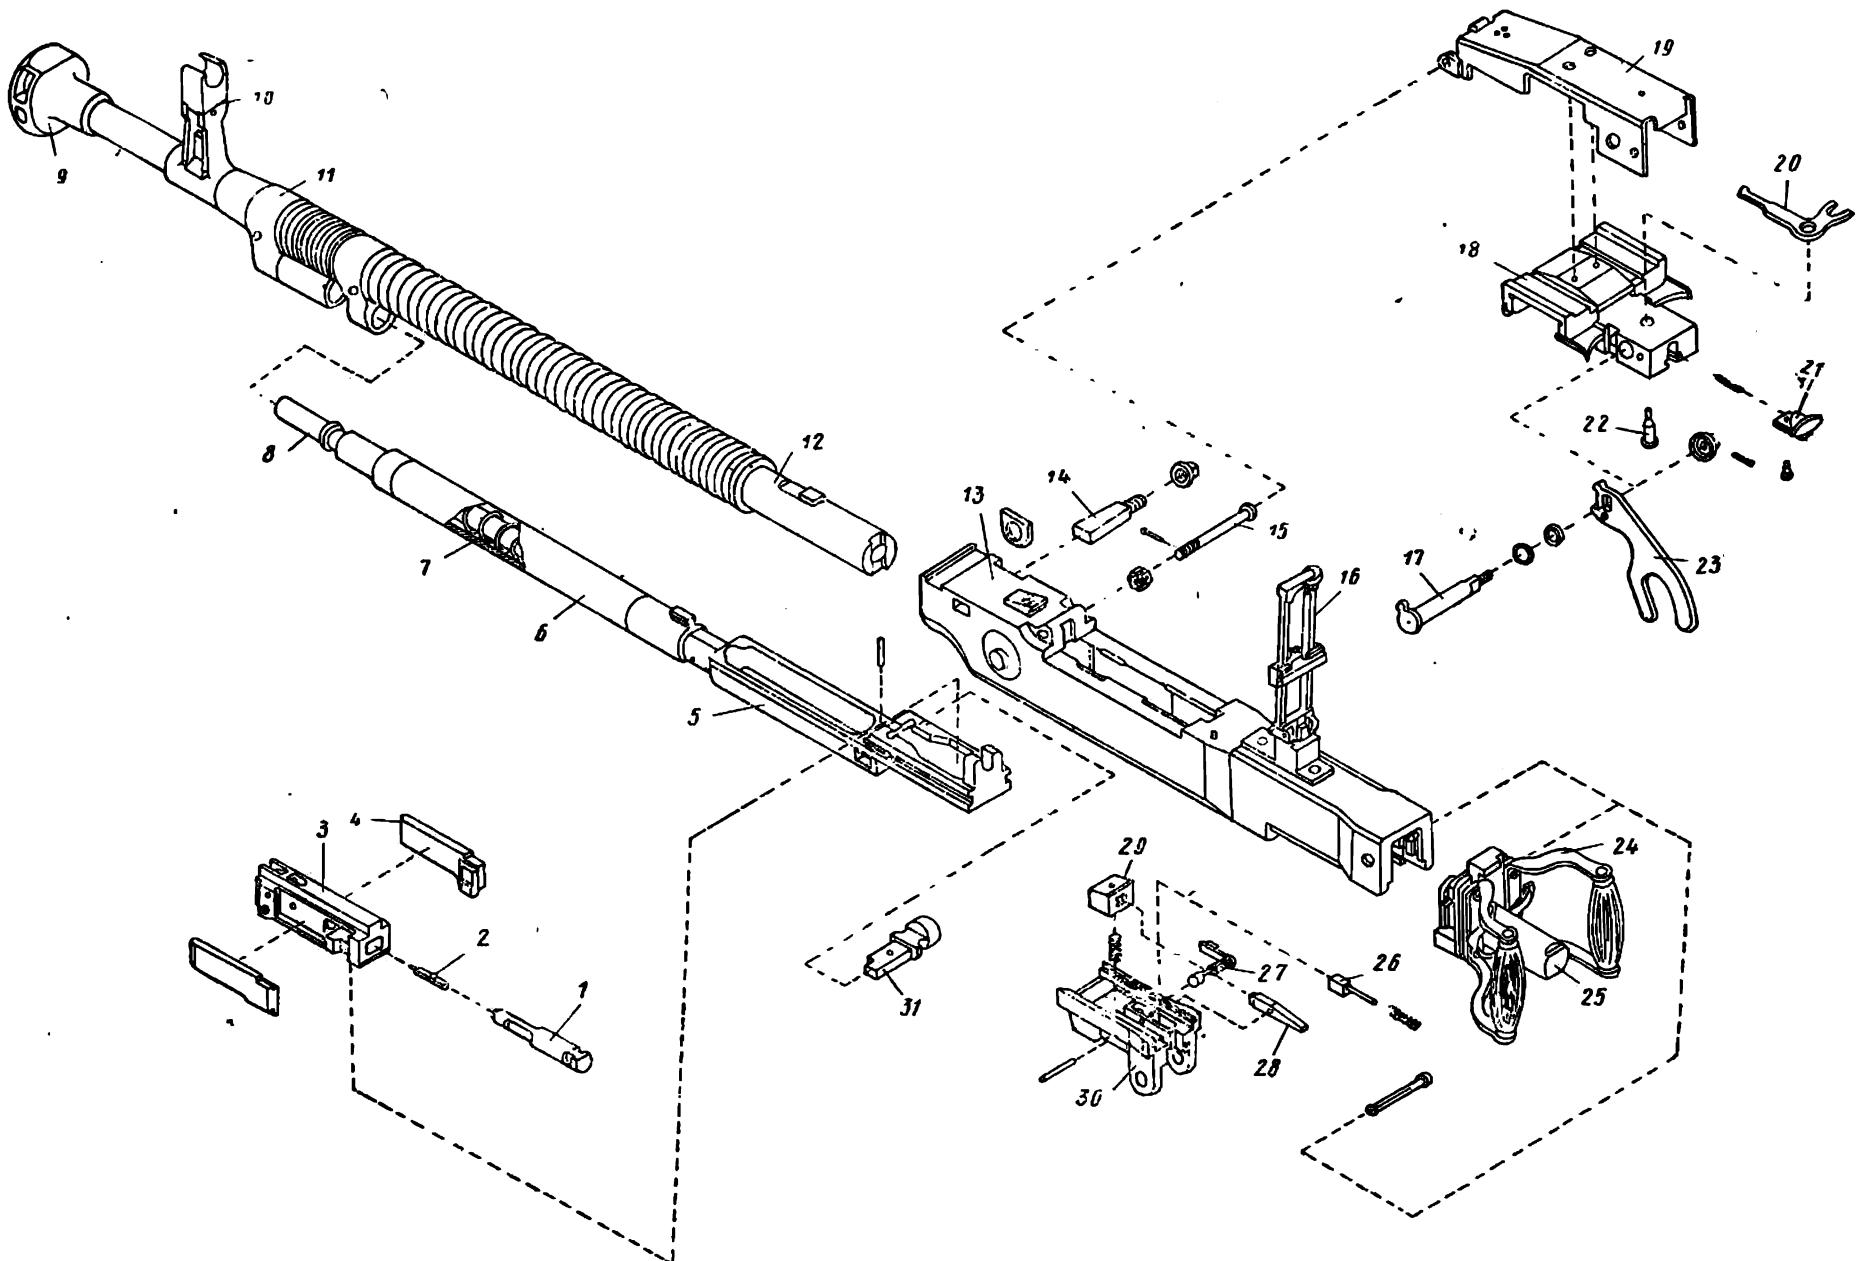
Детали и сборки пулемета ДШКМ:
